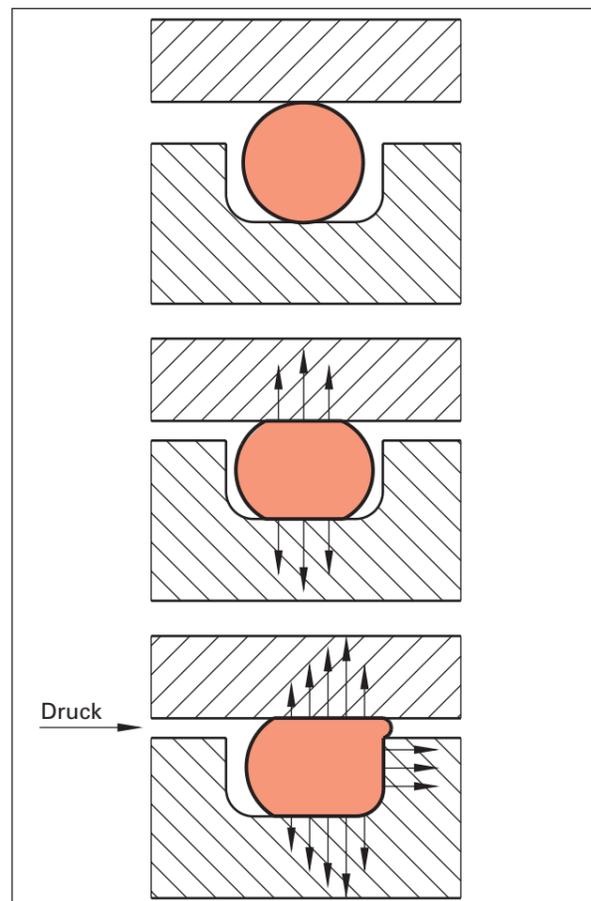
O-Ring-Anpresskräfte mit und ohne Systemdruck
